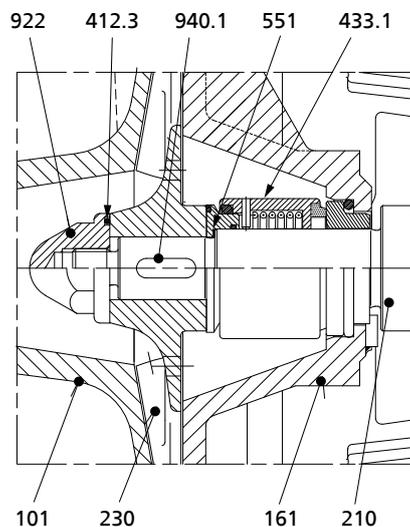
Laufrad einbauen, bei Dichtungstyp H
